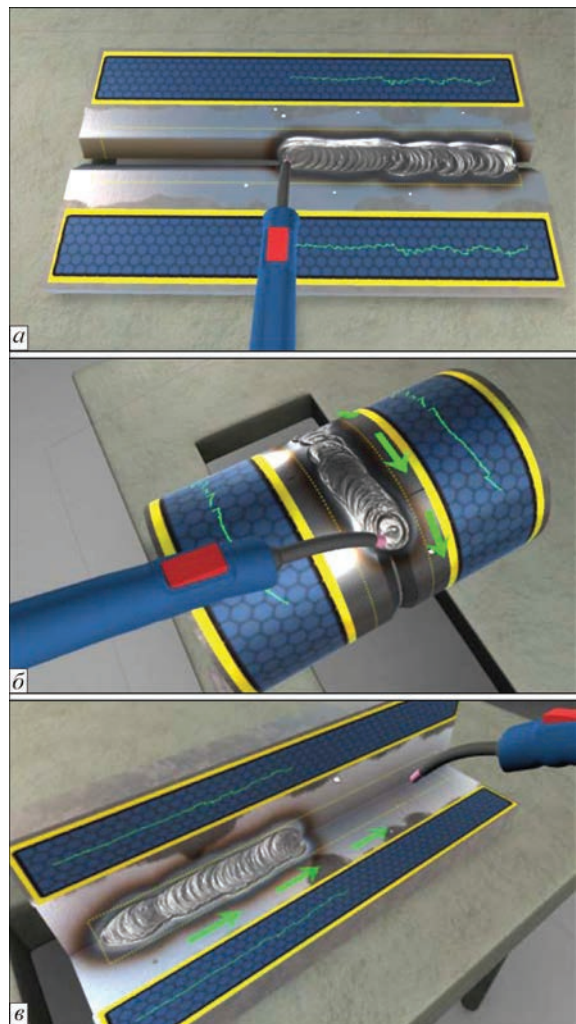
Виртуальная сварка МИГ/МАГ на тренажере V60: *а* — стык в нижнем положении; *б* — орбитальная сварка неповоротного стыка; *в* — угловой шов
